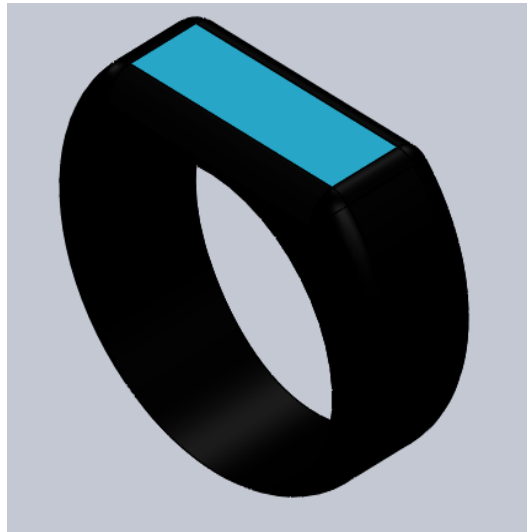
Imagen del diseño CAD de un SmarthWatch 4 Pro [autores]
